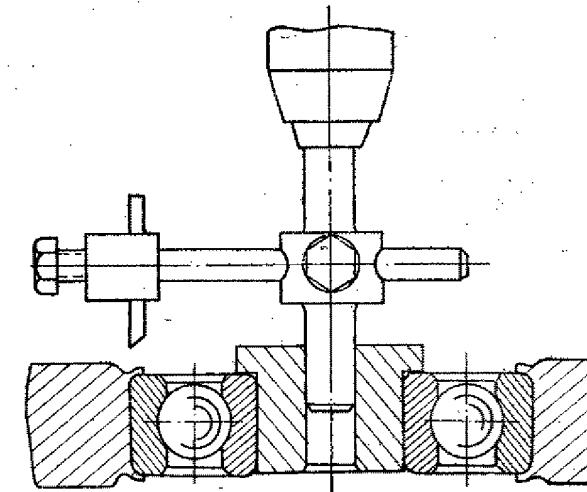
Схема подрезки завальцованных материалов перед демонтажем подшипника
